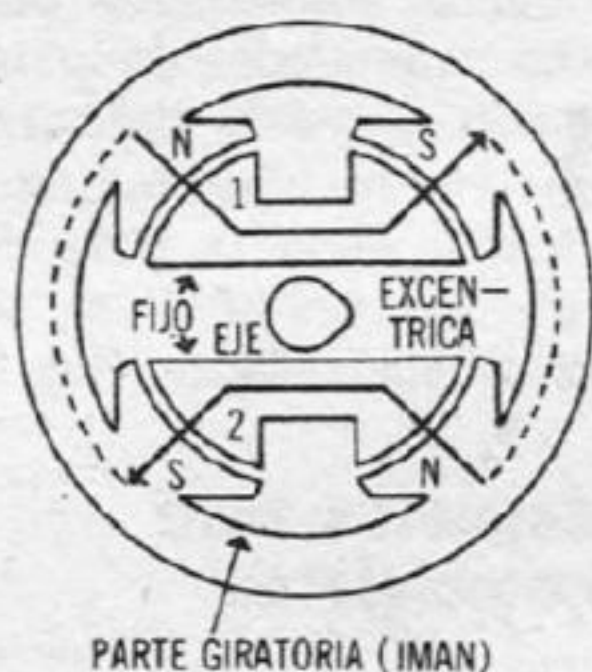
Conjunto del rotor y estator que constituyen el volante magnético.
